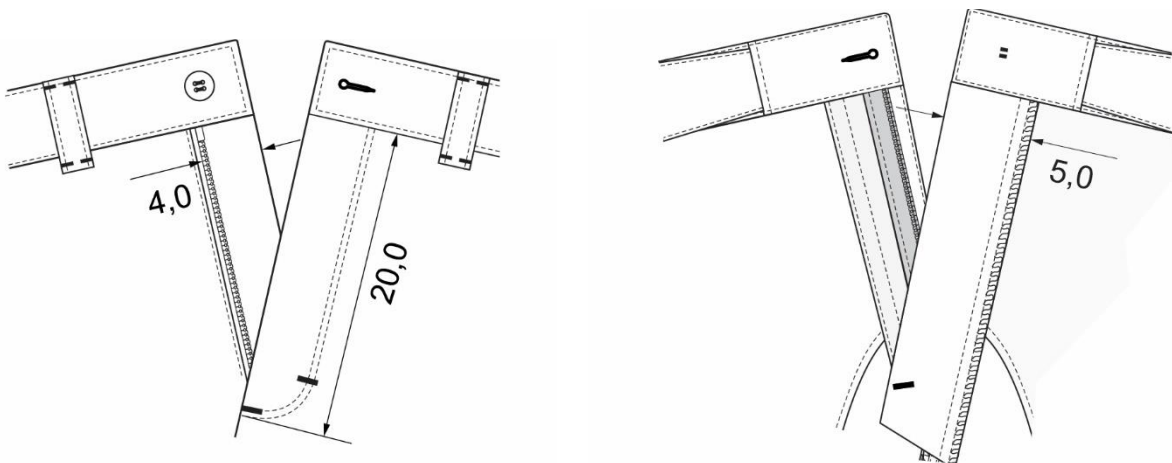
Detalhes da braguilha aberta Figura 11 – Detalhes internos da braguilha
